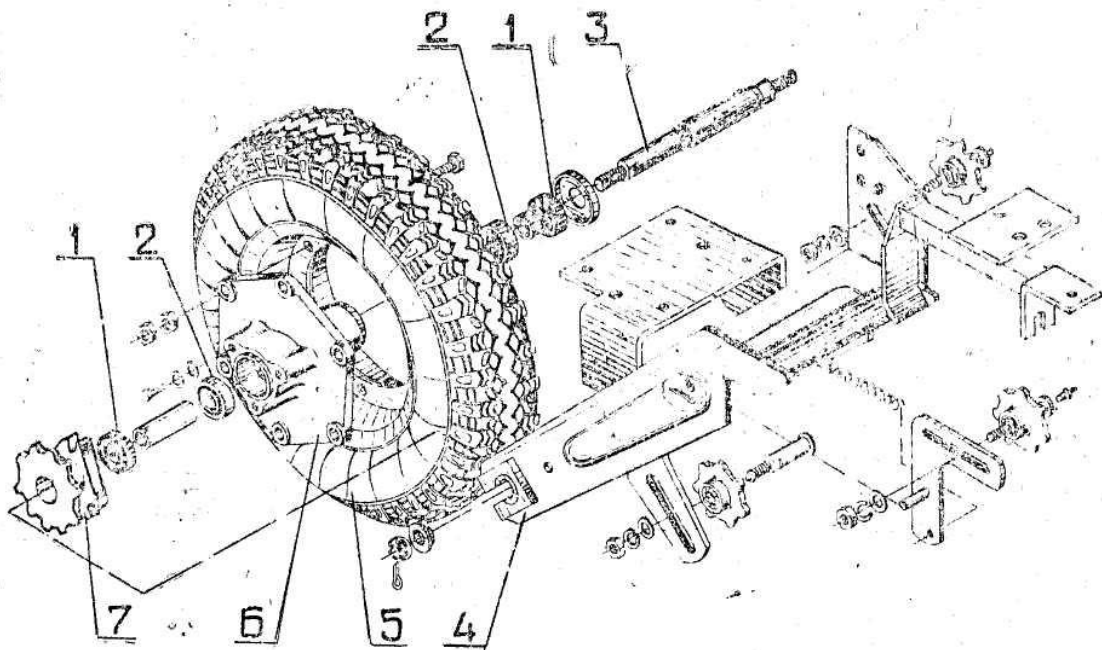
Вузол опорно-приводного колеса бурякової сівалки ССТ-12Б
